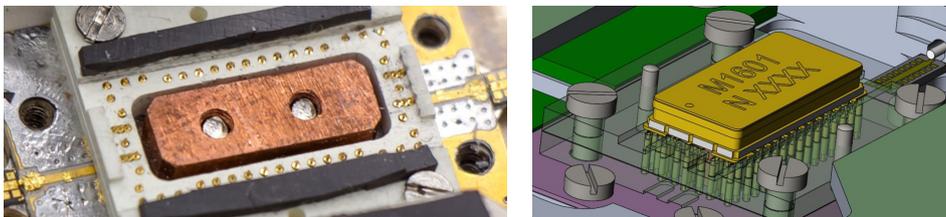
Конструкция контактного устройства для корпусов поверхностного монтажа (фотография - слева и трехмерная модель конструкции - справа)
